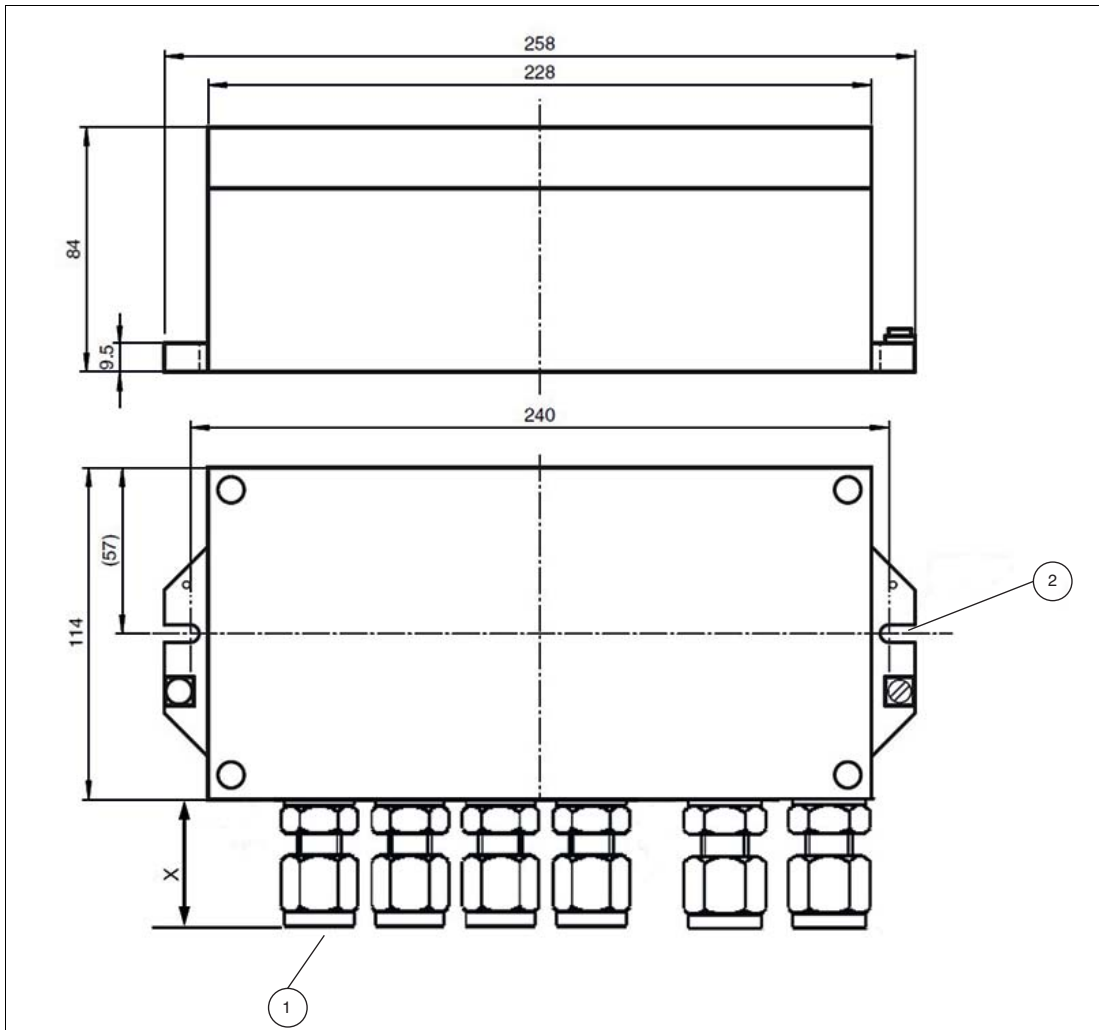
Mechanische Abmessung des F2-Gehäuses
